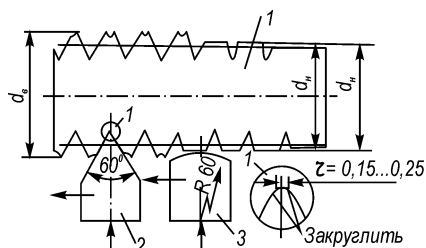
Схема восстановления деталей электромеханическим способом: 1 – деталь;
